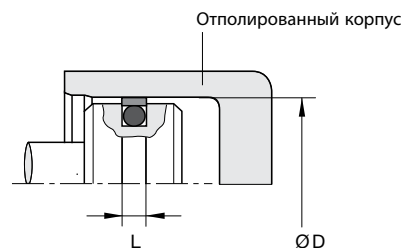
Slipper Seal®поршневого типа, установка, шаг 4. Изменение размера уплотнения Slipper Seal®поршневого типа.
